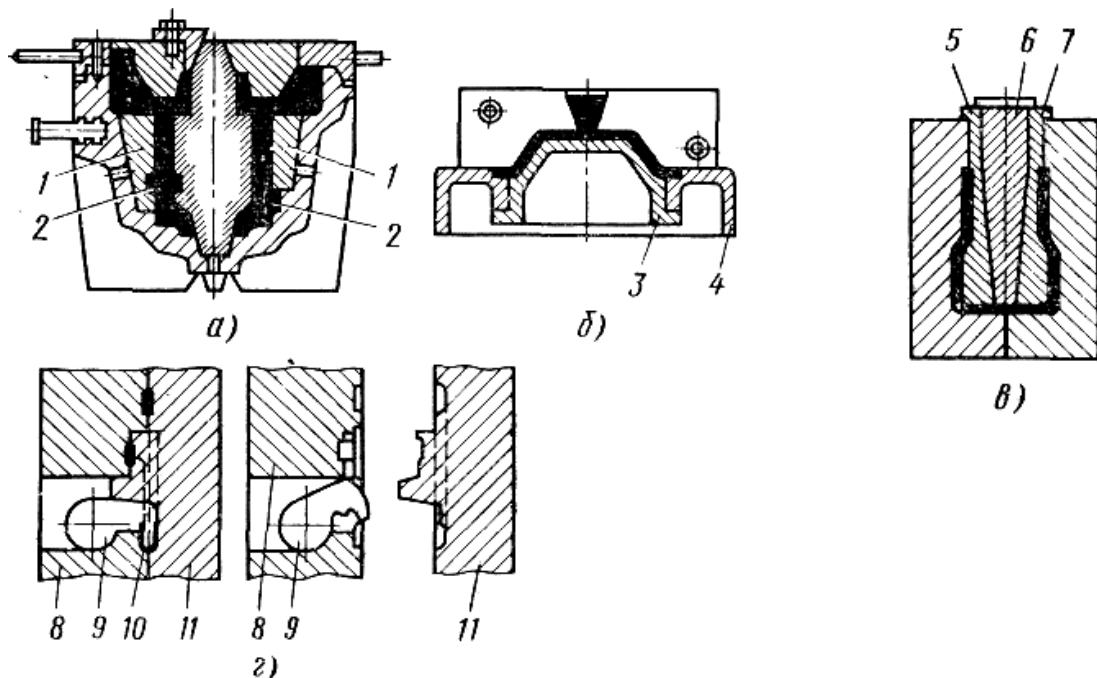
Металеві стрижні: 1 - вкладиш; 2 - виступи на виливку; 3 стрижень; 4 - плита; 5 - 7 - частини стрижня; 8, 11 - напівформи; 9 - поворотний стрижень; 10 – виливок
